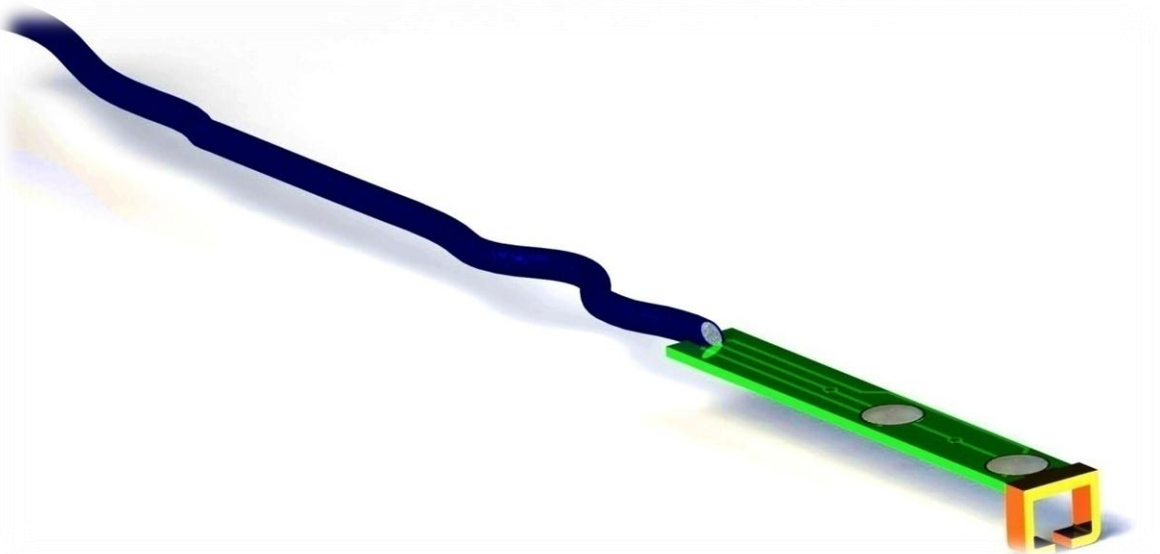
Circuit imprès amb cables i contactors soldats.
